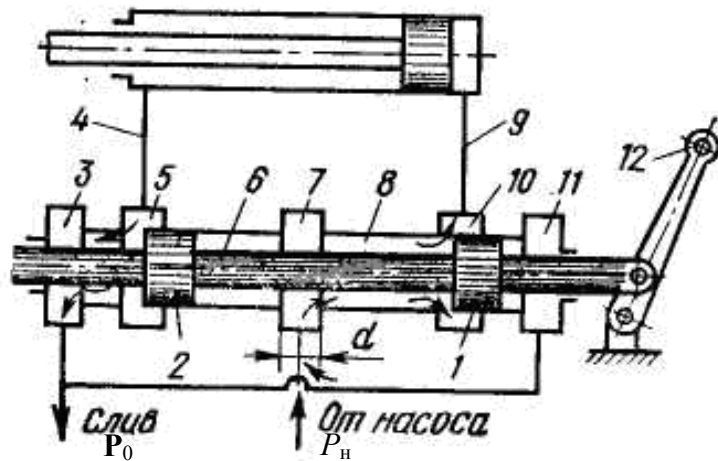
Схема четырехходового золотникового распределителя: 1, 2 – уплотнительные пояски; 3, 5, 7, 10, 11 – кольцевые выточки; 4, 9 – трубопроводы; 6 – плунжер; 8 – корпус золотникового гидрораспределителя; 12 – рукоятка для ручного реверсирования двигателя гидроцилиндра; P_n – давление на входе распределителя со стороны насоса; P_0 – давление на сливе; d – диаметр уплотнительного пояса
